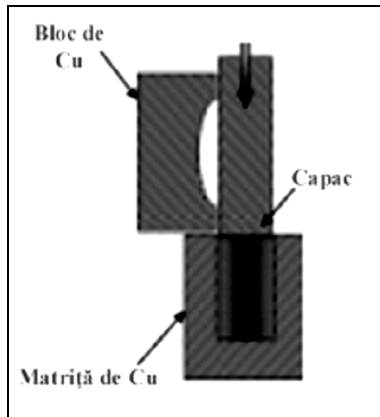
Principiul turnării cu capac (prelucrată din [5])
